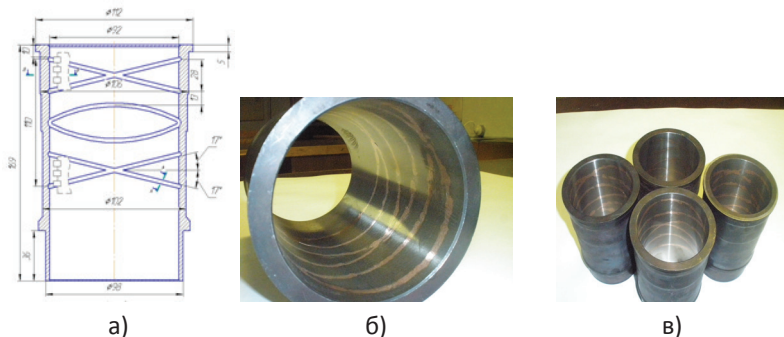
Гильза цилиндра с изменёнными физико-механическими характеристиками: схема гильзы; металлизированная гильза; комплект металлизированной ЦПГ
